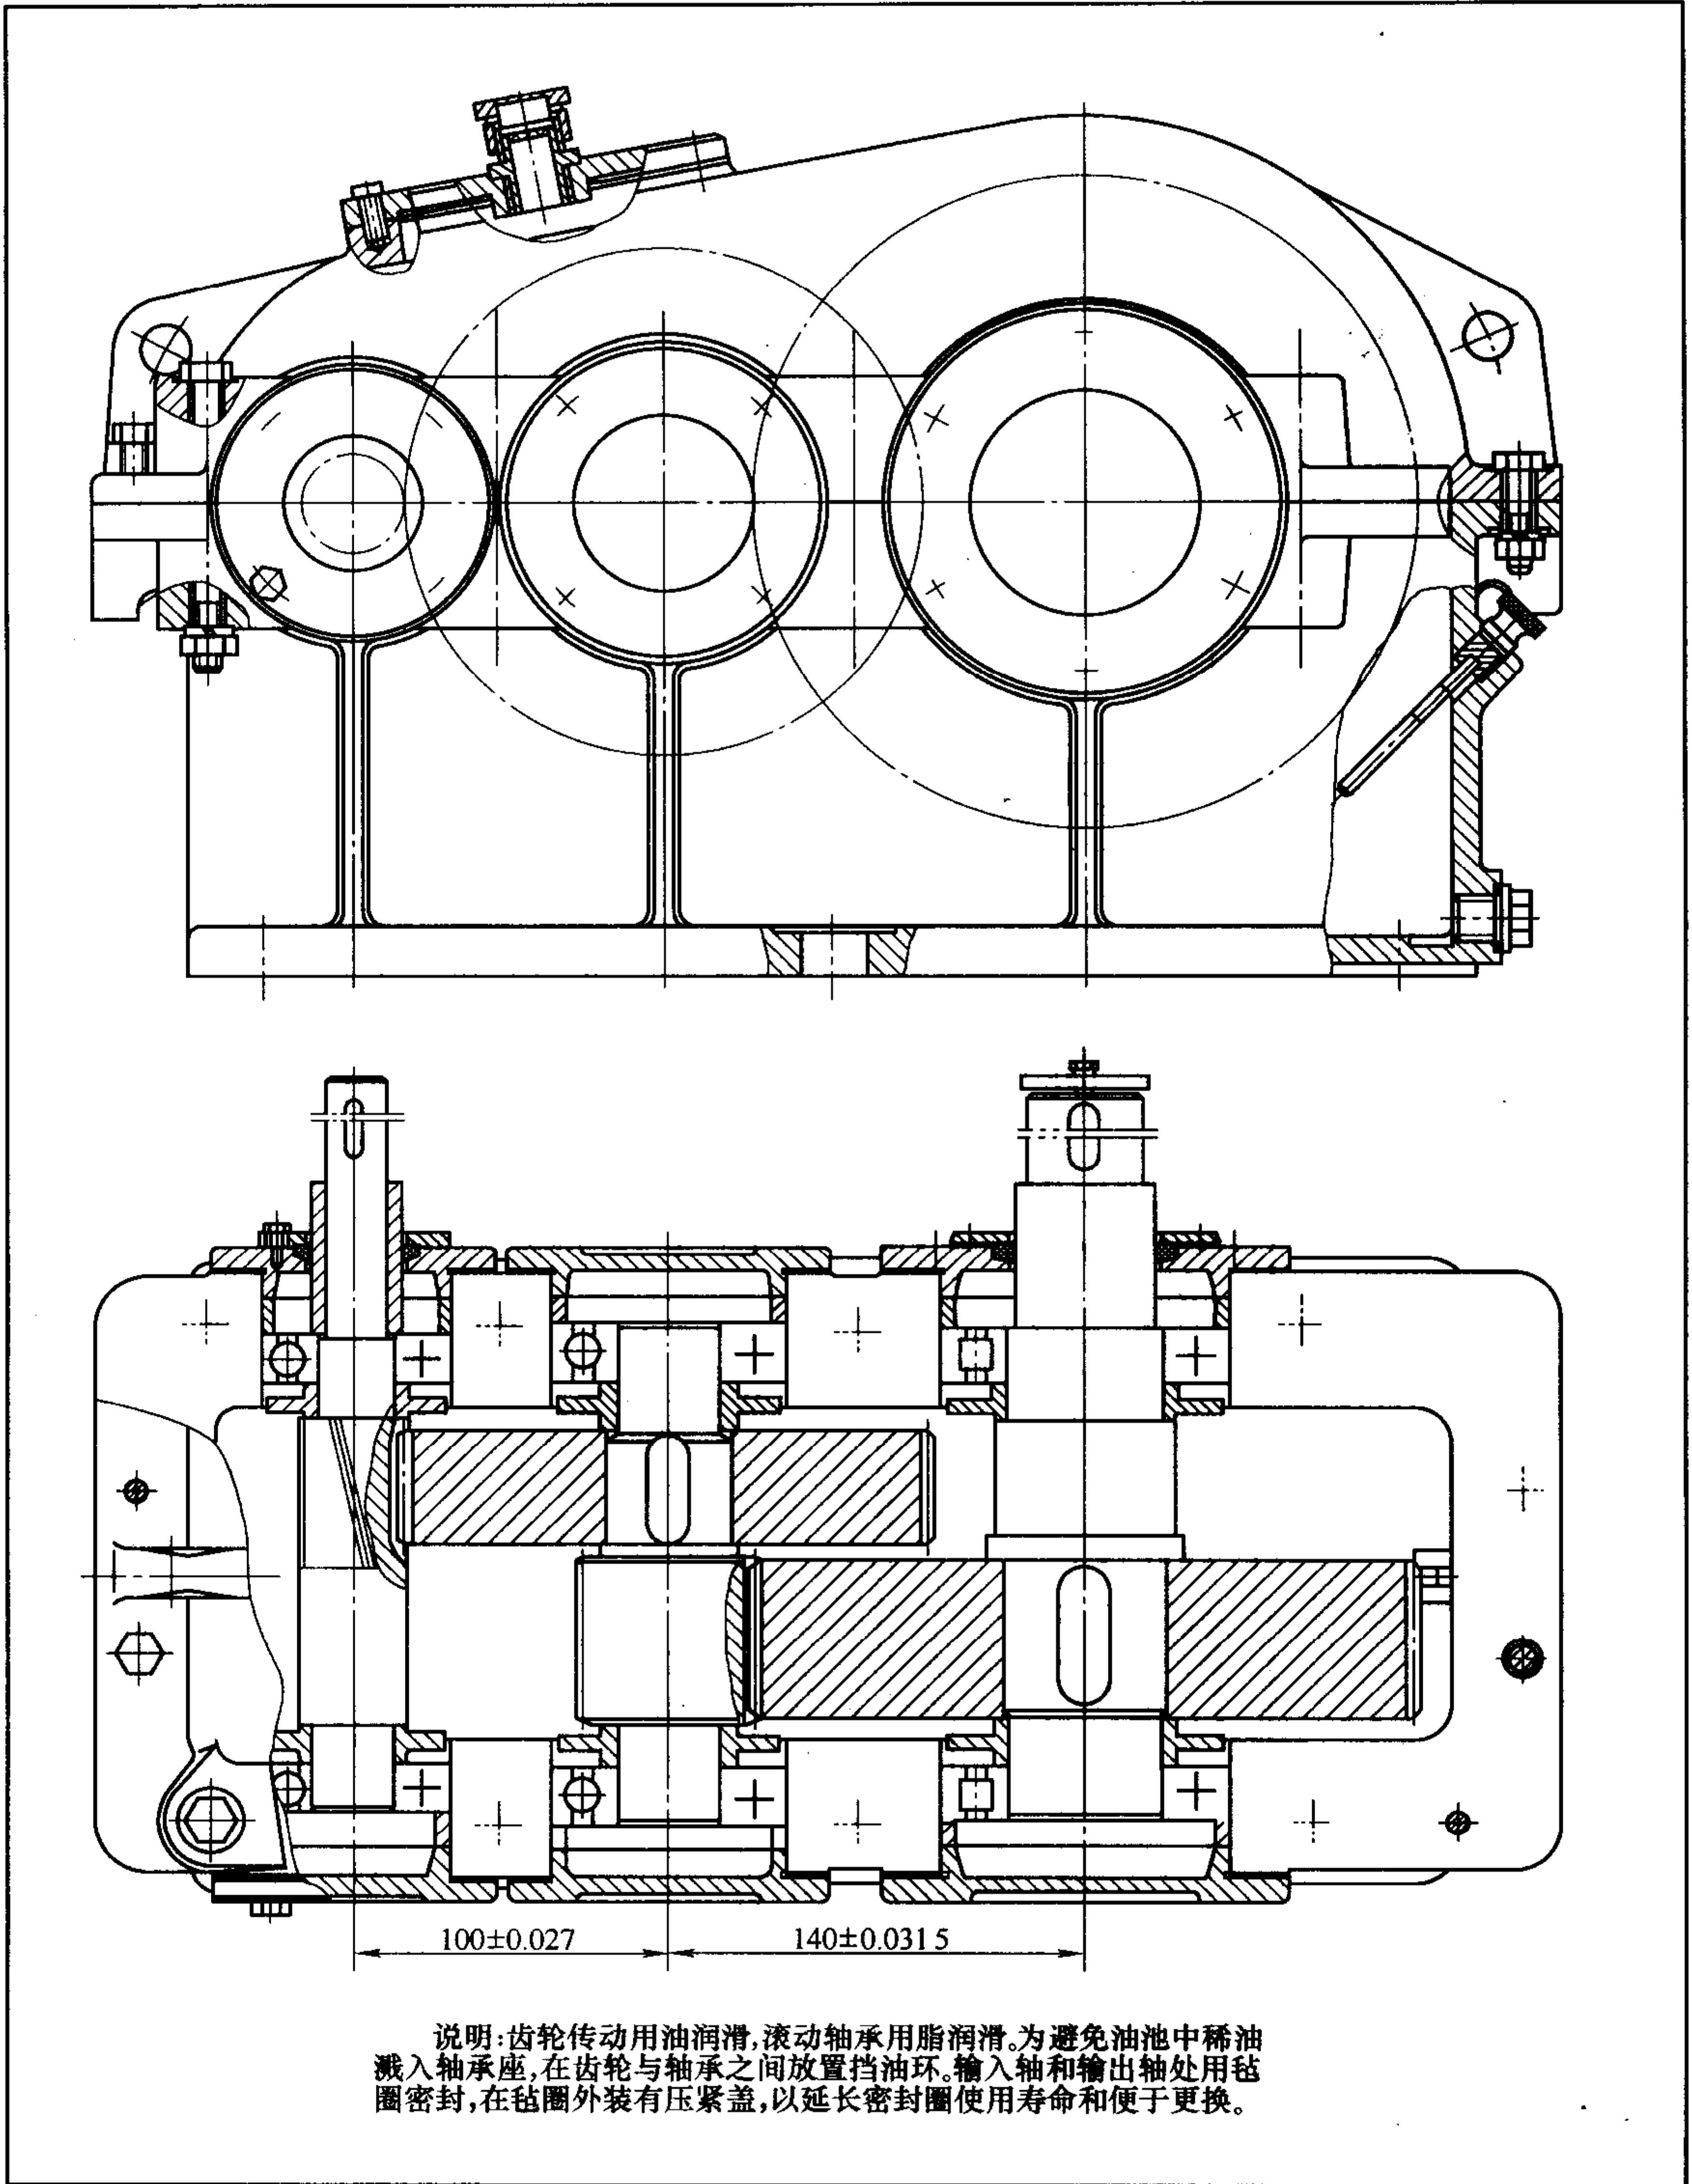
16 二级圆柱齿轮减速器结构图(展开式)
